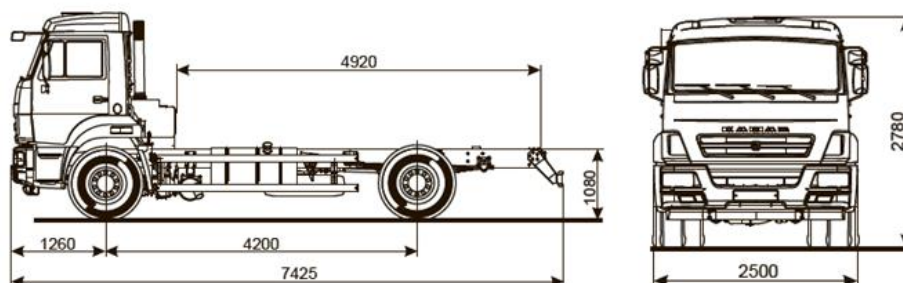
Габаритные размеры шасси КАМАЗ 43253
